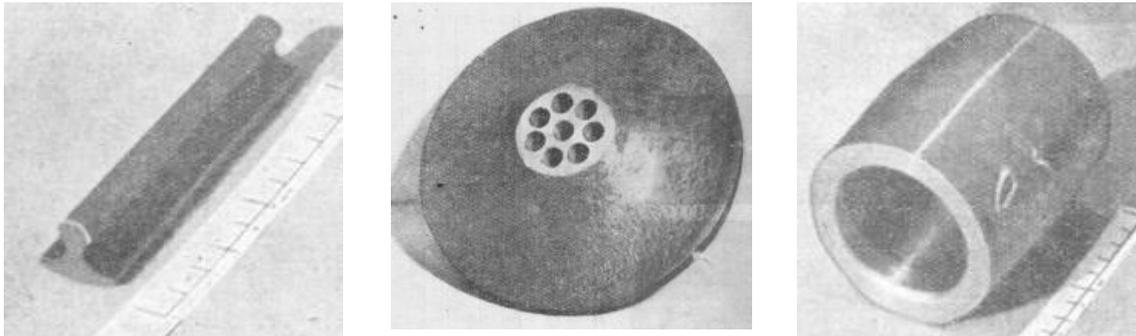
Dispositivos empleados en el sistema SGTM.
